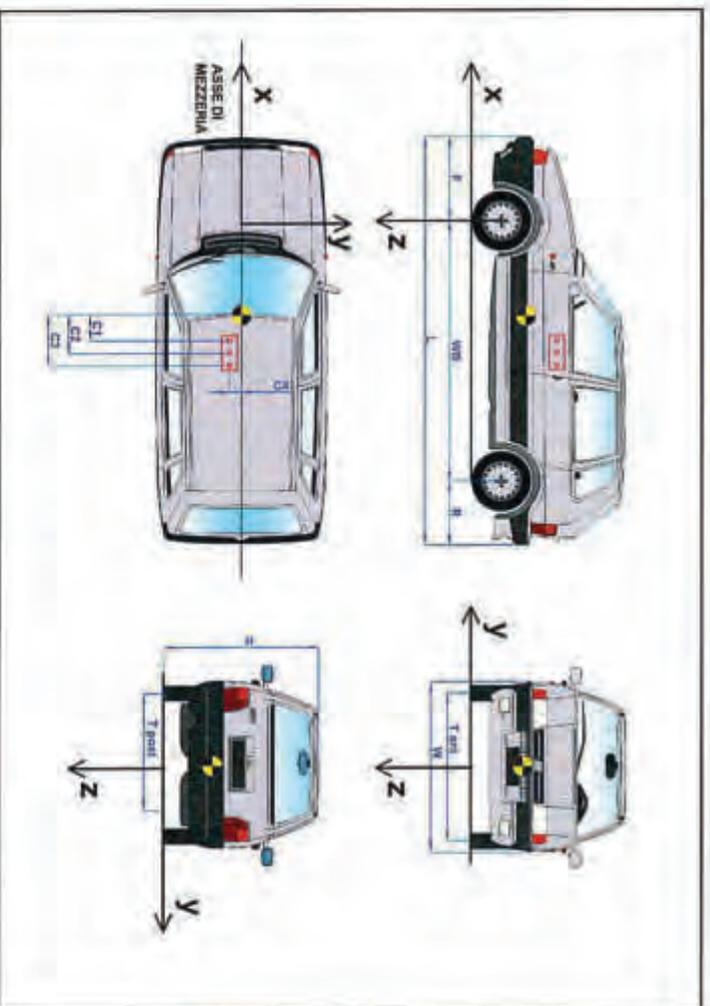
Figure 3 Dimensioni del veicolo – Vehicle dimensions
